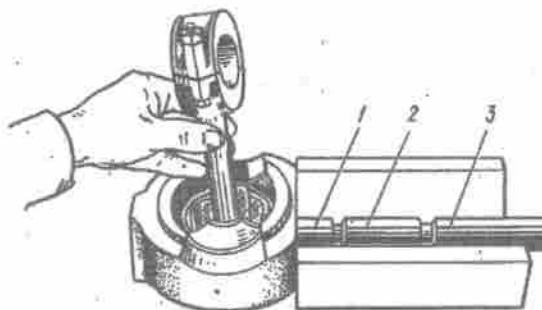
Vorrichtung zum Einpressen des Kolbenbolzens:
